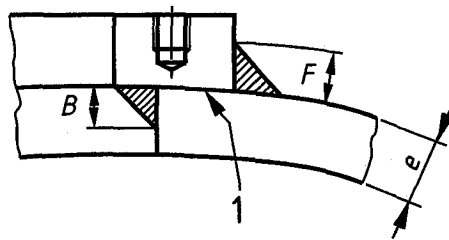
Typische Ausführungen von aufgeschweißten Anbauteilen
